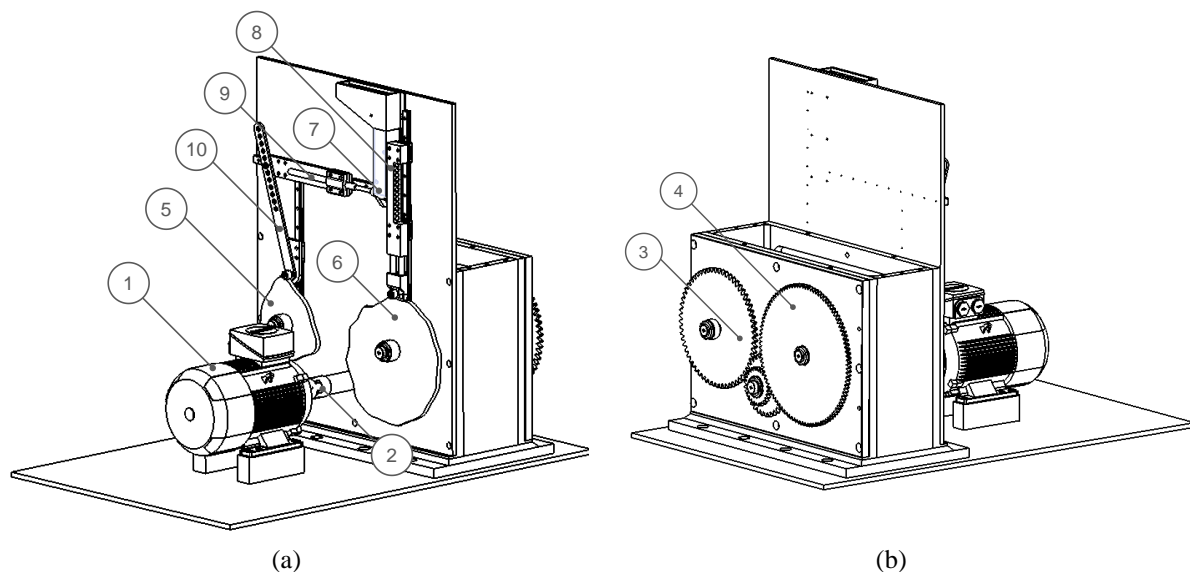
Diseño de la máquina didáctica para poner en práctica el conocimiento de levas y engranajes: (a) vista frontal, lado levas y (b) vista trasera, lado engranajes.
